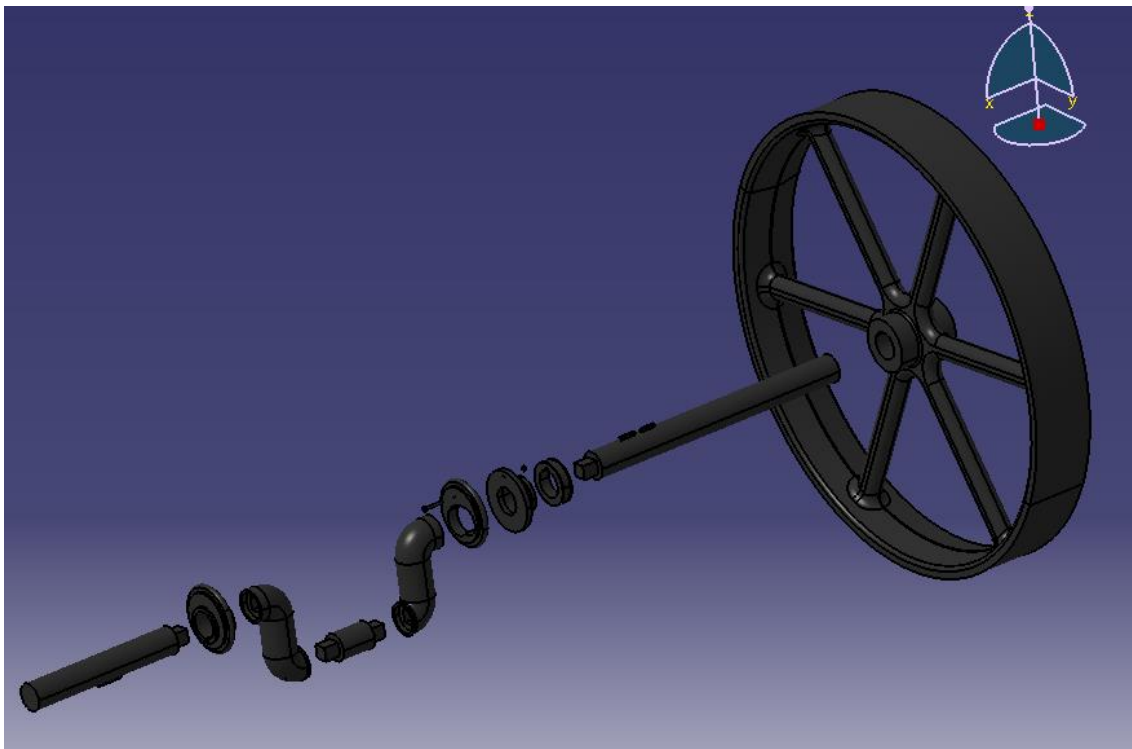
Conjunto cigüeñal y volante de inercia explosionado
